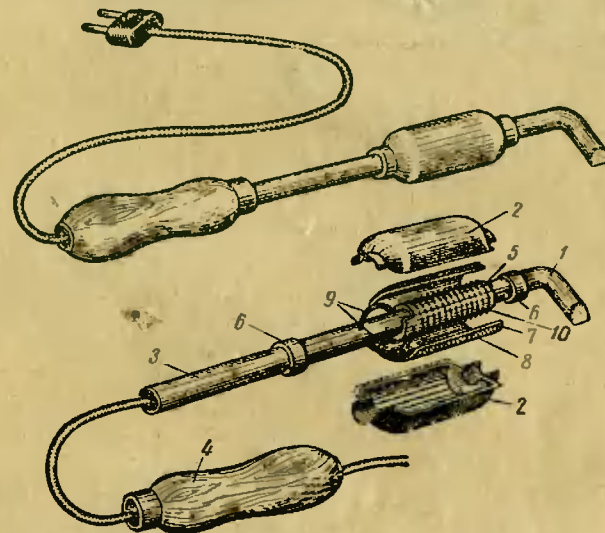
Электрический паяльник и его детали: 1 — рабочий стержень, 2 — крышка кожуха, 3 — металлическая трубка, 4 — ручка, 5 — первый слой слюды, 6 — кольцо для закрепления кожуха, 7 — второй слой слюды, 8 — слой шнурового асбеста, 9 — концы соединительного шнура, покрытого асбестом, 10 — нихромовая спираль.
